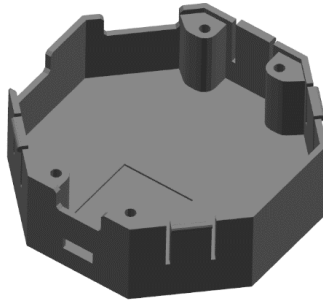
Diseño de caja para la tarjeta de adquisición.
